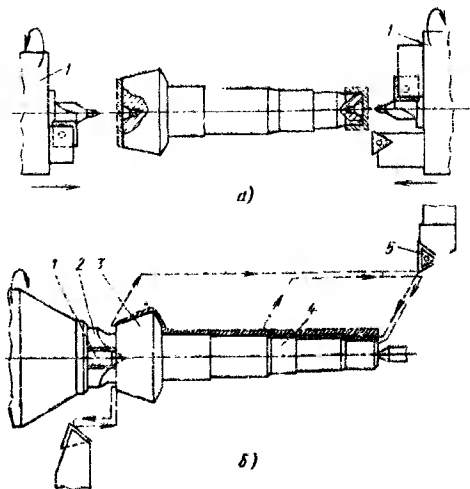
Схемы обработки заготовки конического колеса-вала:
